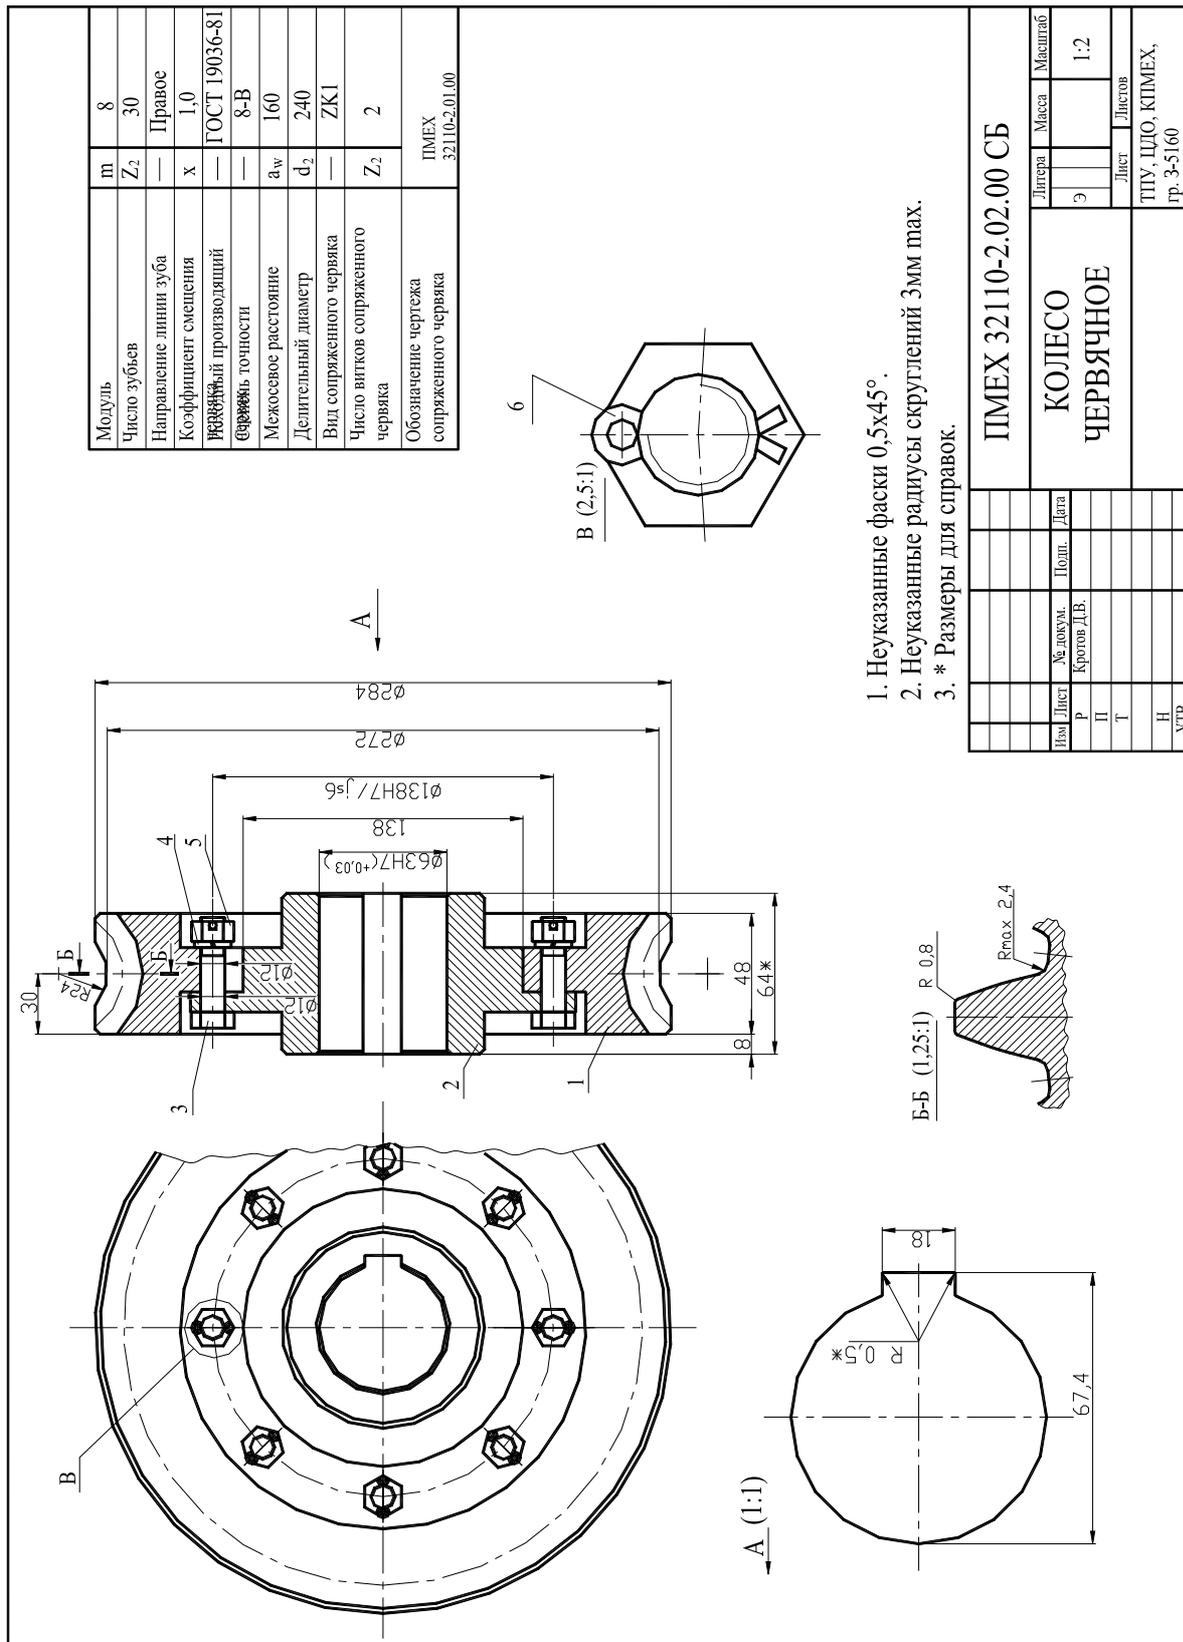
Пример выполнения эскизного чертежа червячного колеса
